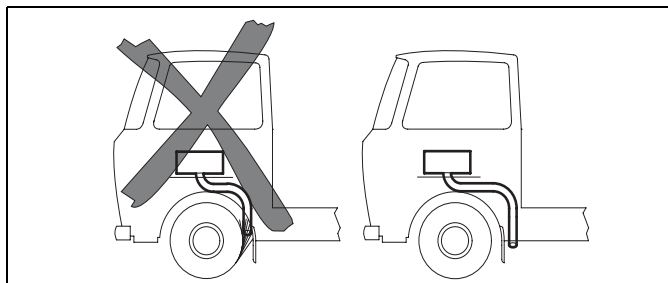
Éviter toute obstruction provoquée par un encrassement
